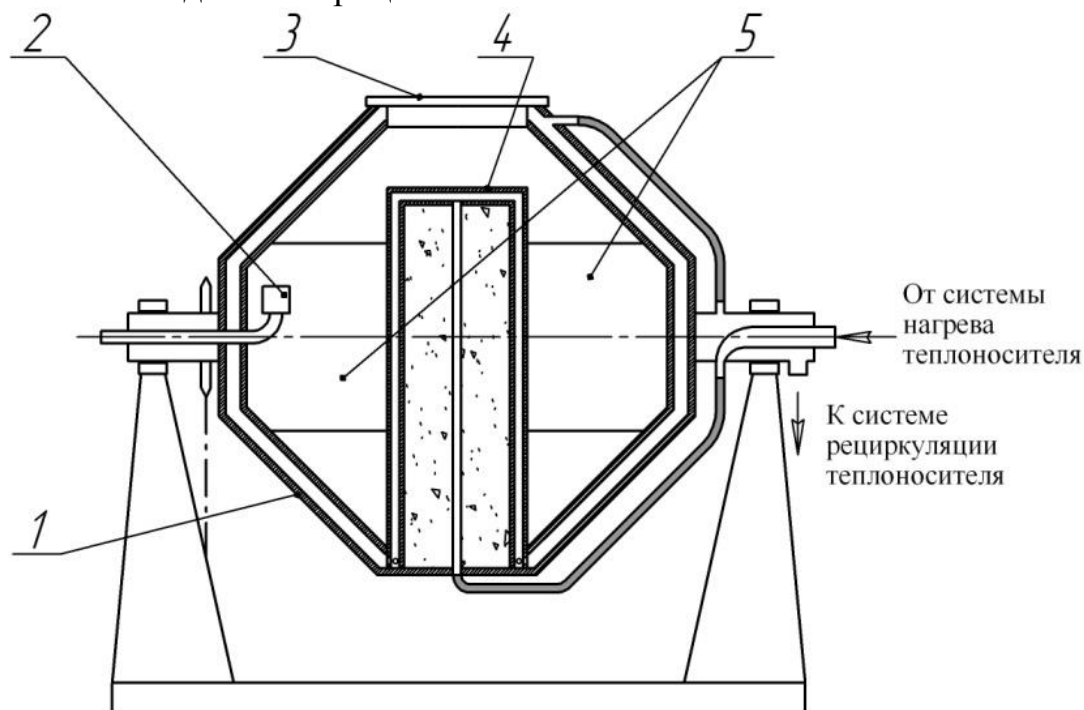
Обжарочный аппарат с цилиндрическим вытеснителем
